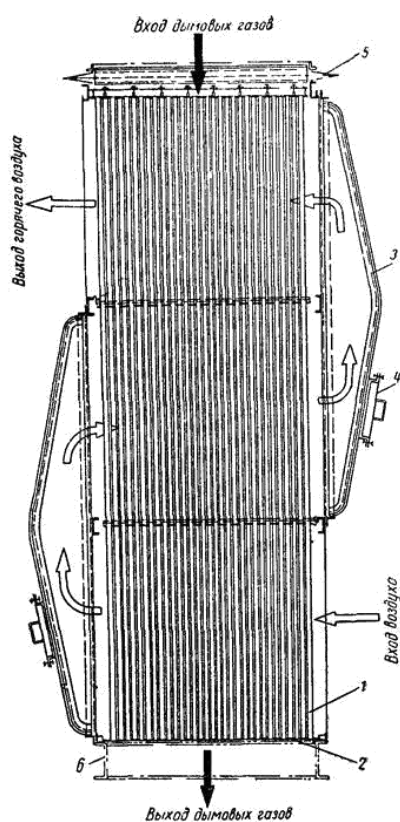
Трубчатый воздухоподогреватель: 1 – трубы; 2 – нижняя трубная доска; 3 – перепускной короб для воздуха; 4 – люк; 5 – компенсатор;
